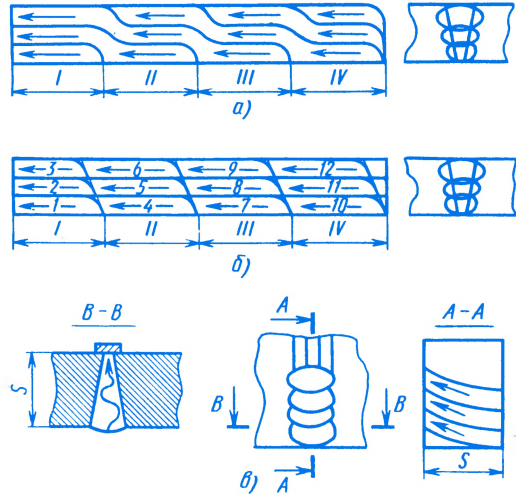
Схемы заполнения шва при сварке: а — каскадом, б — блоками, в — поперечной горкой; 1—12 — слои в шве, I, II, III, IV — ступени шва, S — толщина стыка
